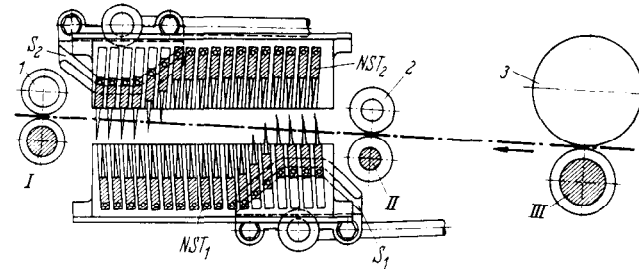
Steuerung der Nadelstabfelder durch Steuerschlösser
